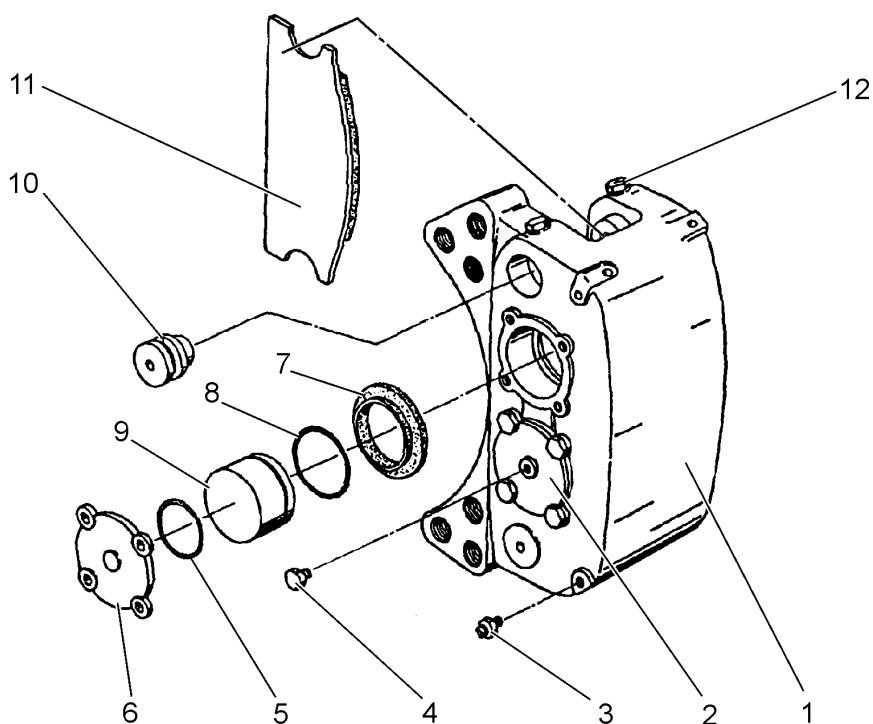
Суппорт (головка) рабочего тормоза (вид)
